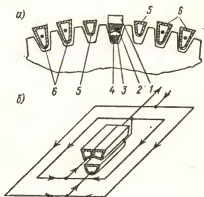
Индуктор для нагрева впадины шестерен среднего модуля одно-временным способом: а — расположение проводов; б — схема соединения индуктора:
